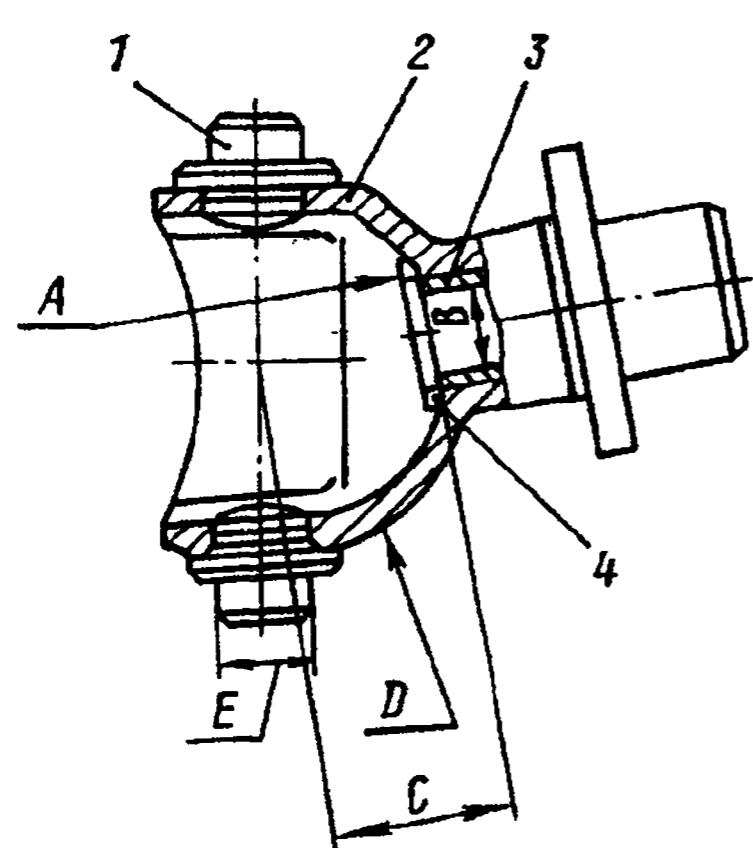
Опора шаровая поворотного кулака в сборе:
